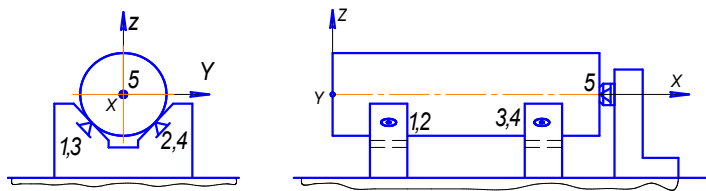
Схема базирования цилиндрической заготовки на токарном станке
